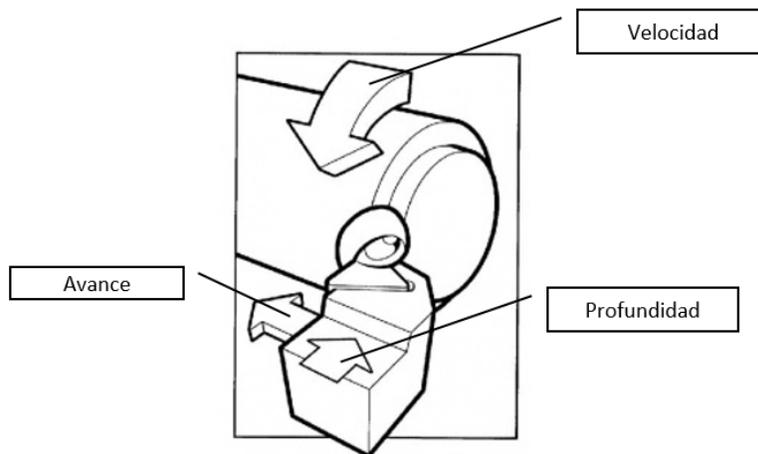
Parámetros de corte en el proceso de torneado [Tomado de " wiki.ead.pucv.cl/Casiopea"]
